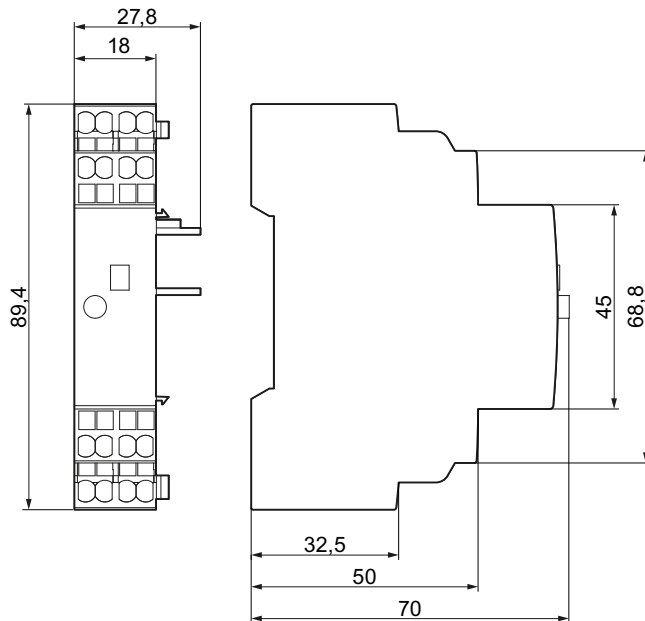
Meldeschalter 3RV2921-2M (Federzuganschlusstechnik)
